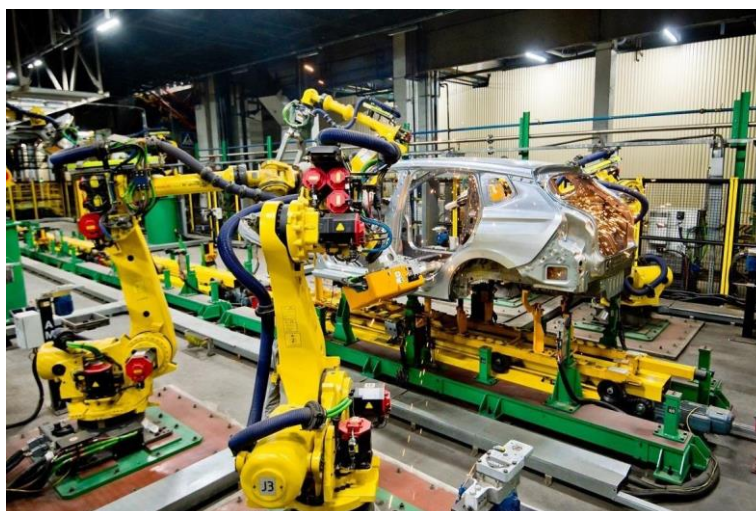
Сварка кузова автомобиля роботами
